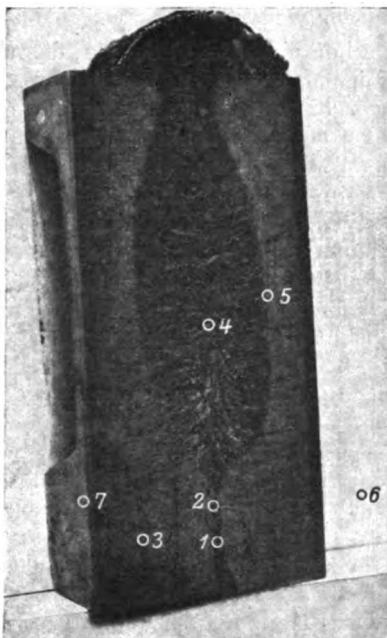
Schnitt der Schweißung längs der Stegmitte. $V = \frac{1}{2}$ fach. Die Ziffern im Gefügebild bezeichnen die Stellen der nachfolgenden mikroskopischen Aufnahmen.
